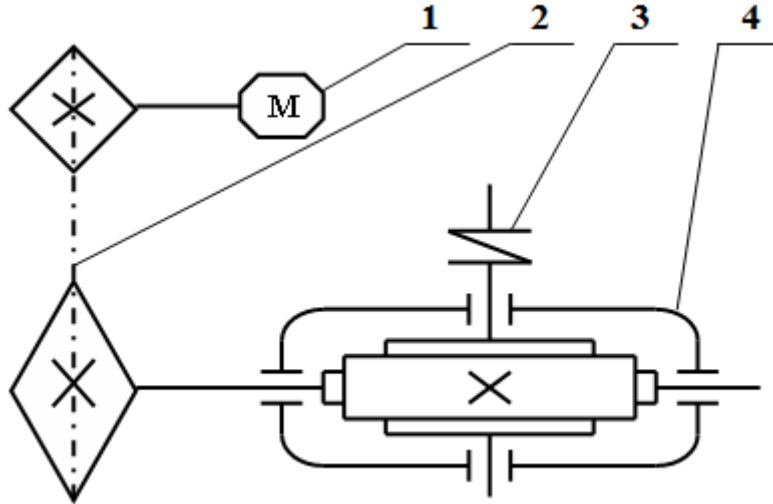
Привод вібраційного конвеєра: 1 – електричний двигун, 2 – ланцюгова передача, 3 – муфта типу МПВП, 4 – одноступінчатий черв'ячний редуктор з нижнім розташуванням черв'яка.
